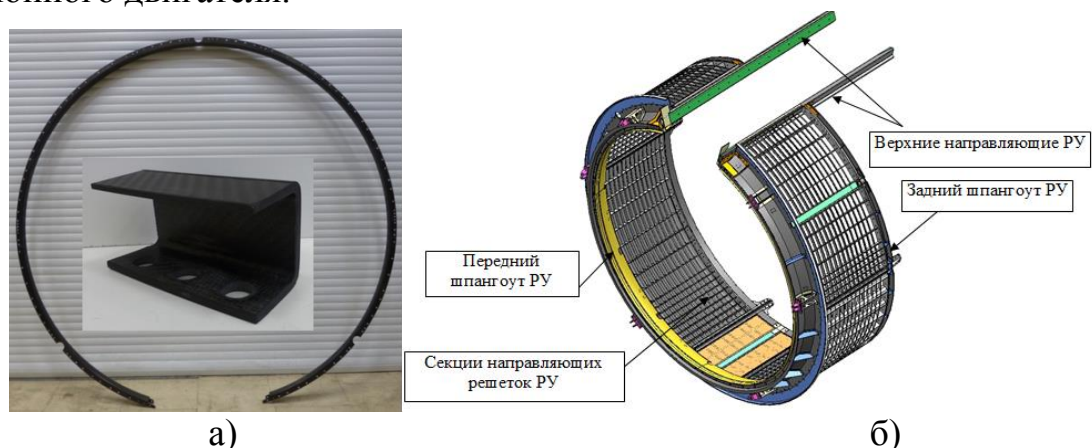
Общий вид заднего шпангоута реверсивного устройства из ПКМ (а), силовой каркас реверсивного устройства (б)
